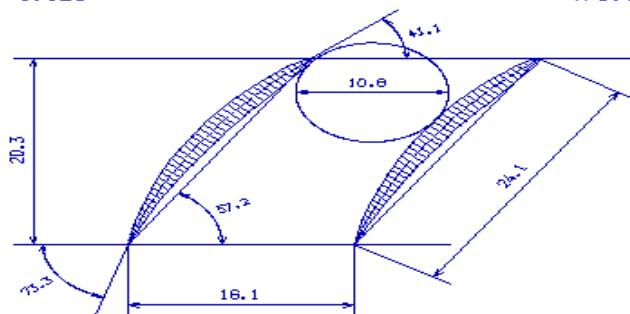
Решетки профилей рабочего колеса компрессора
